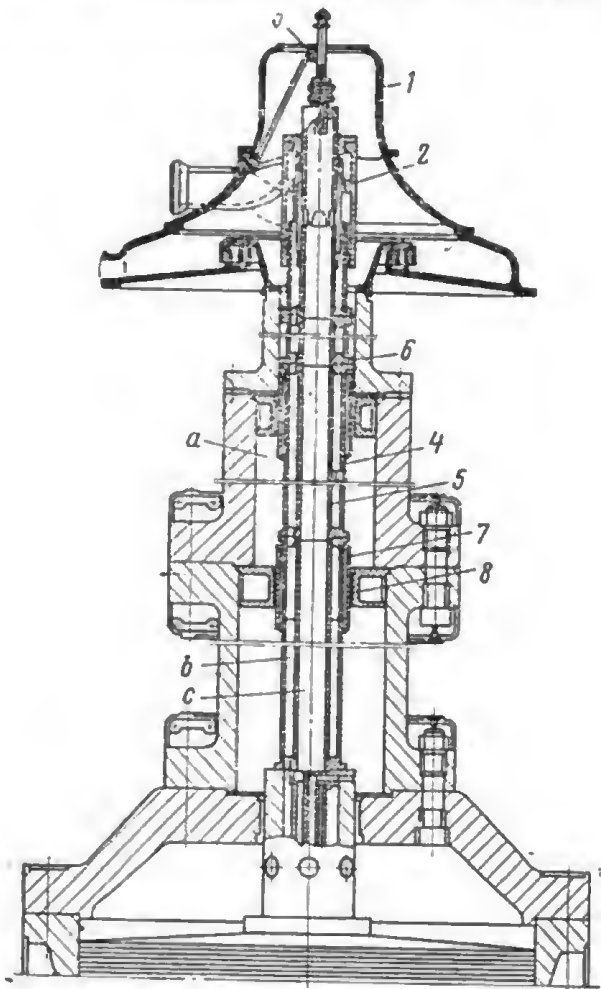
Схема подвода масла к сервомотору рабочего колеса.
